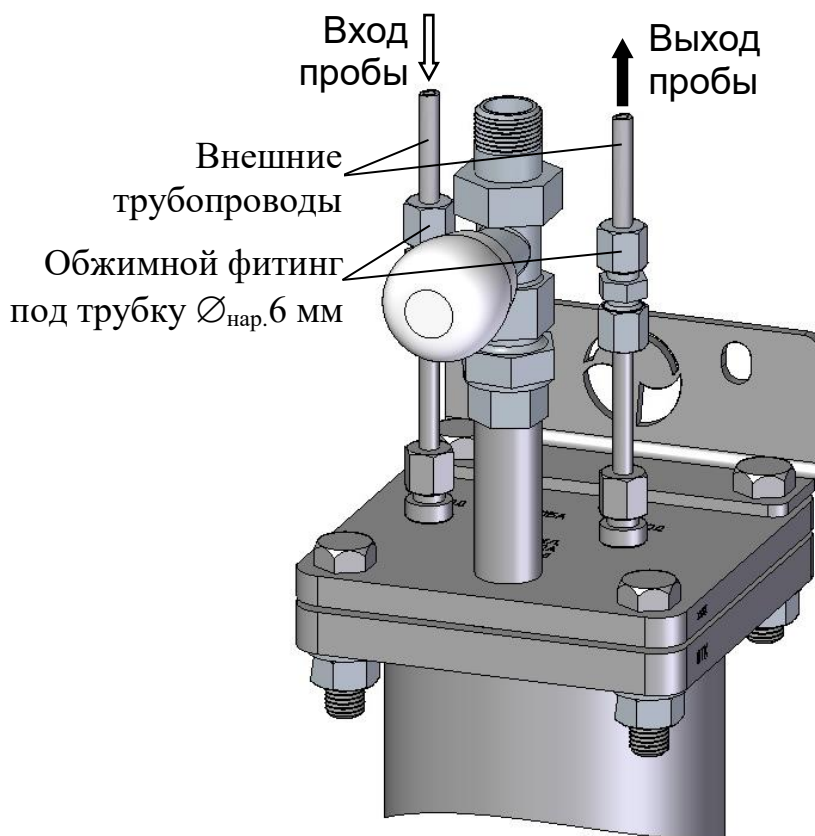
Подсоединение внешних трубопроводов к ТО с арматурой
